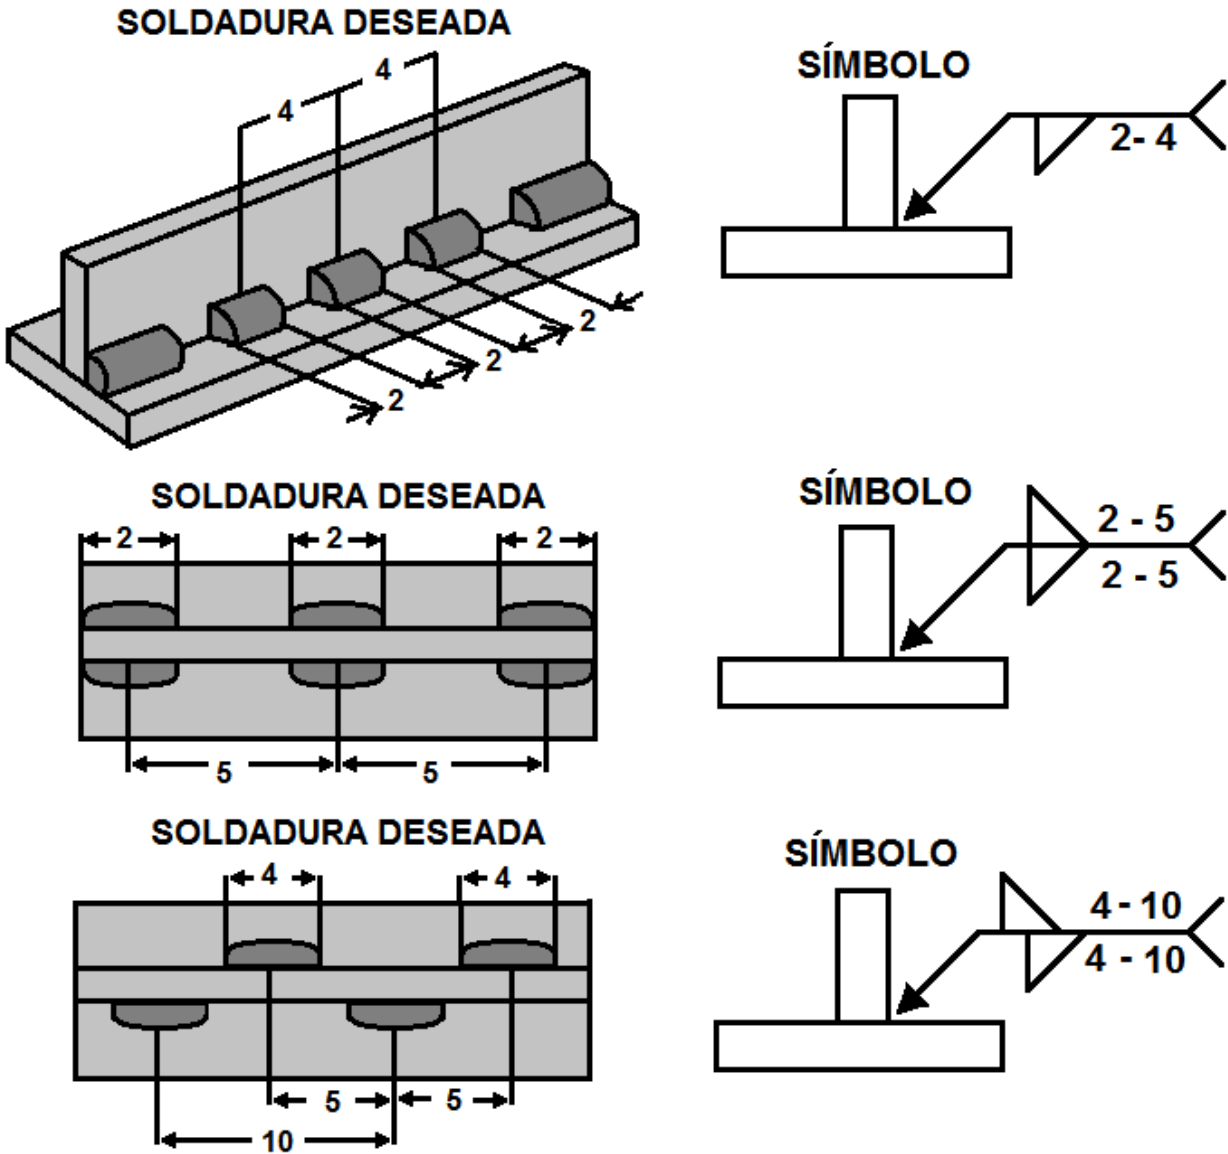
Dimensiones en soldadura discontinua (3, 8, 18, 31)
